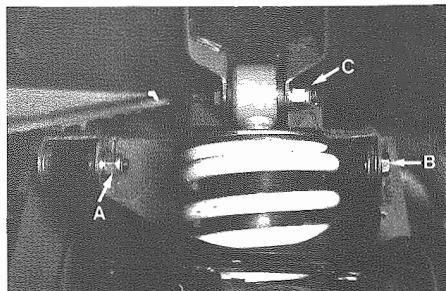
A - Viti fissaggio braccio sup. al telaio
